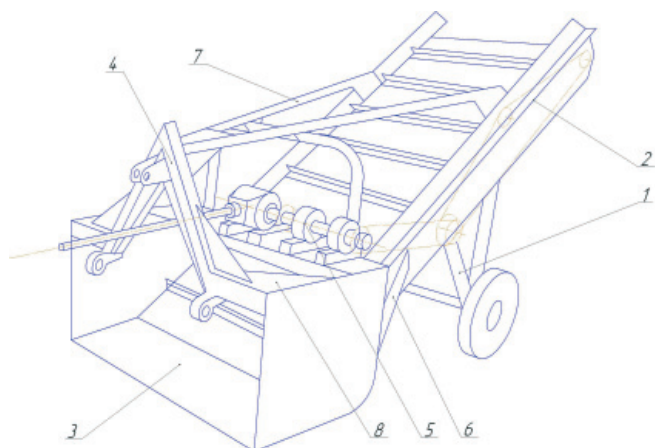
Схема машины для удаления и погрузки почвы: 1 – несущая рама; 2 – транспортер; 3 – ковш; 4 – механизм навески; 5 – механизм привода; 6 – нижняя тяга; 7 – верхняя тяга; 8 – верхняя стенка ковша
